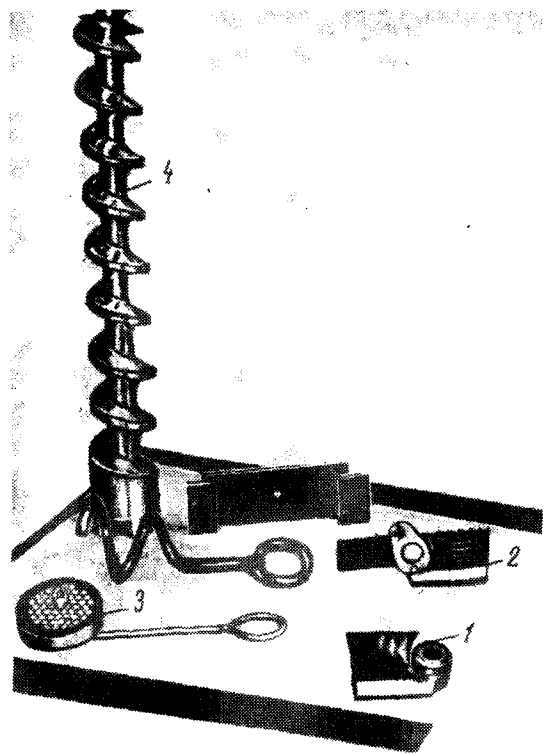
Экструдер для влажного прессования кортлендской смеси:
